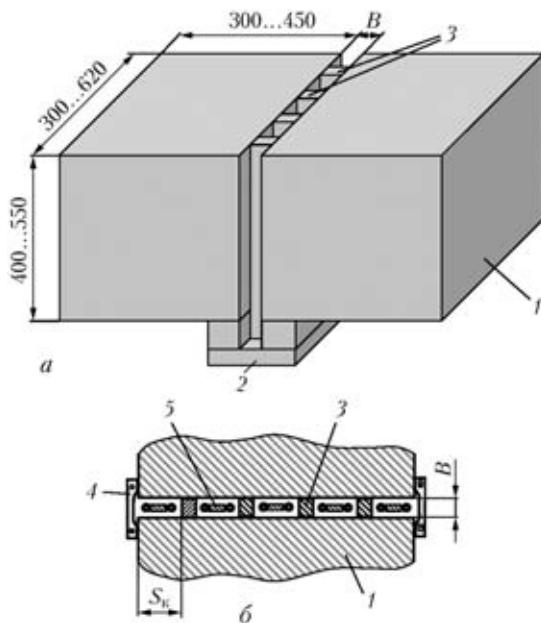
Схема сборки (а) и МЭШС (б) опытных образцов с продольной установкой плавящихся мундштуков: 1 — свариваемые детали; 2 — входной карман; 3 — формирующие пластины-проставки; 4 — водоохлаждаемая накладка; 5 — плавящийся мундштук;  $B$  — ширина сварочного зазора;  $S_k$  — толщина металла колодца
